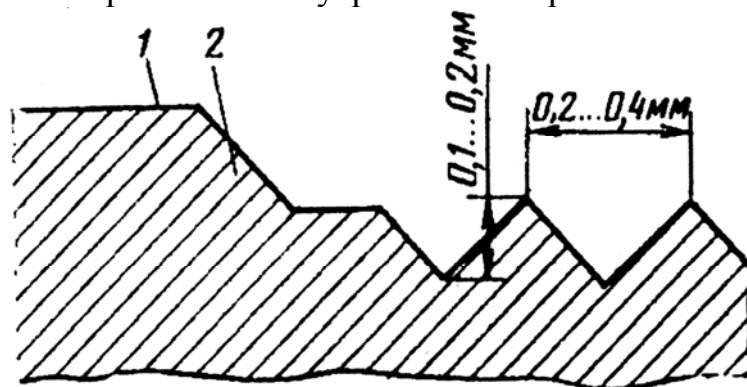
Подготовка поверхности способом нарезания рваной резьбы:
